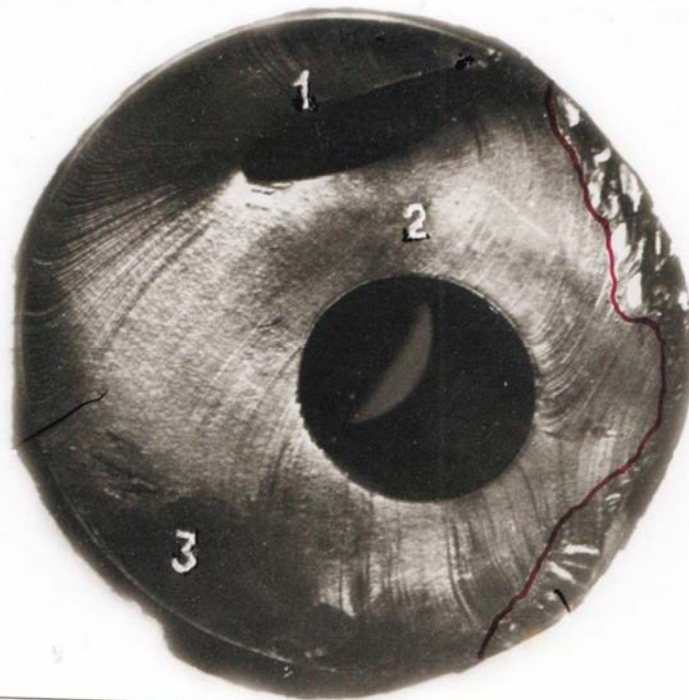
Усталостный излом шатунной шейки коленчатого вала:
